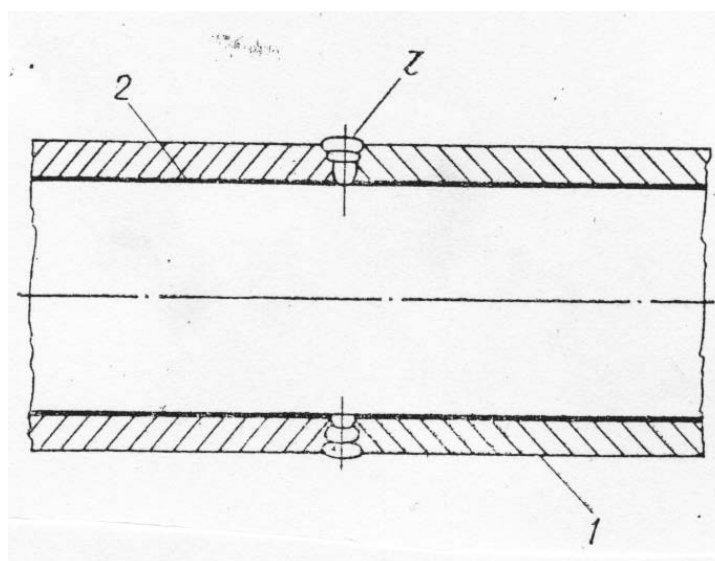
Внешний вид стыкового соединения, используемого при сварке остеклованных труб: 1 - основной металл трубы, 2 - остеклованное покрытие, 3 - сварной шов.
